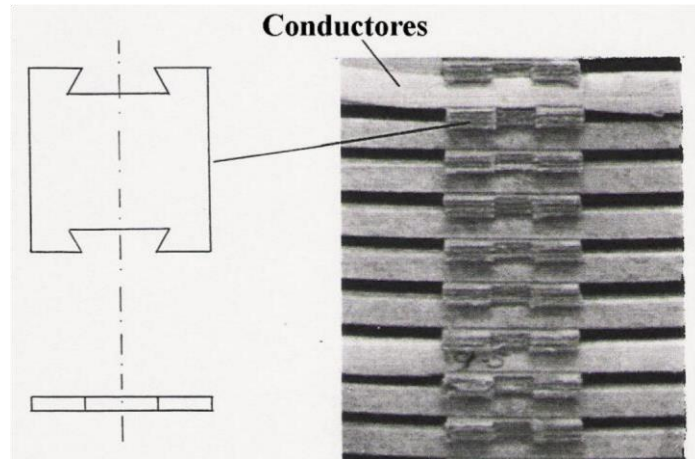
Aislamiento para separación de secciones de conductores. (a) Geometría del aislamiento. (b) Colocación en el devanado
